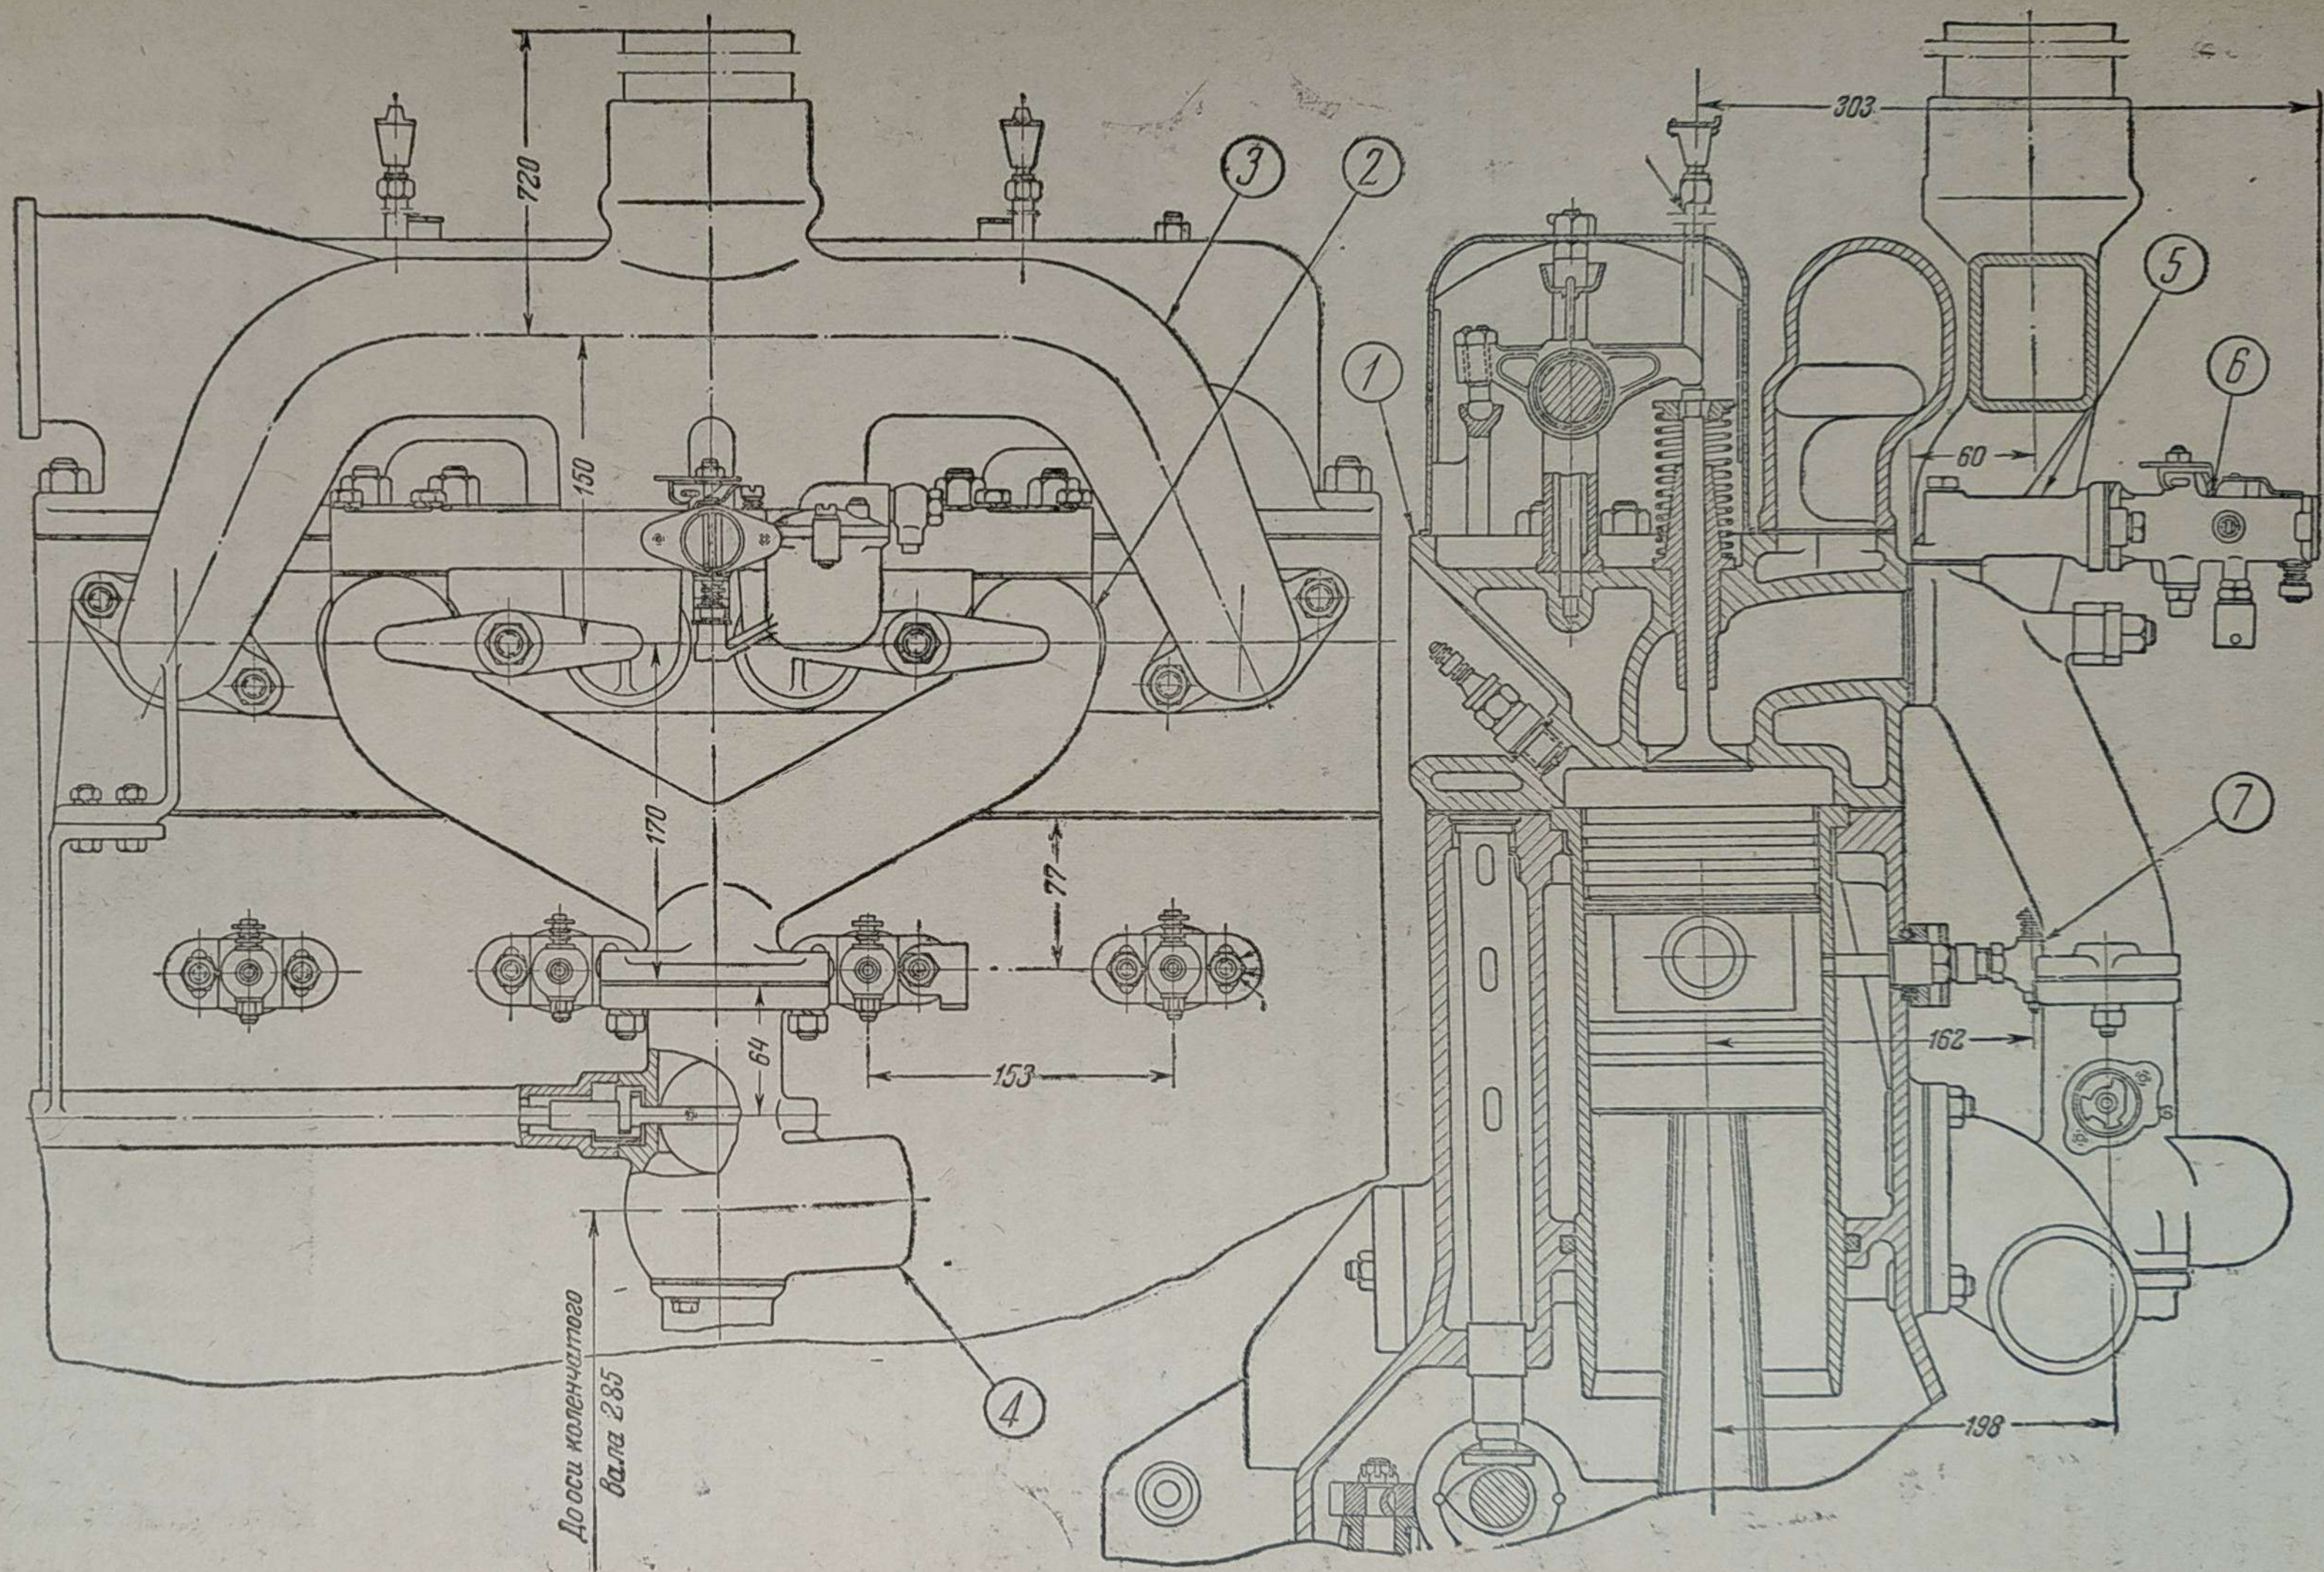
Общий вид газового двигателя колесного трактора СХТЗ-15
